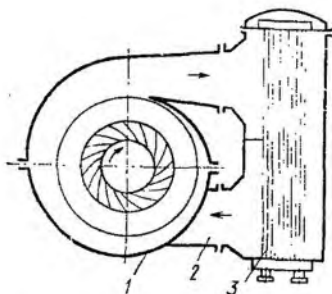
Схема подключения промежуточного холодильника к обеим частям корпуса компрессора
